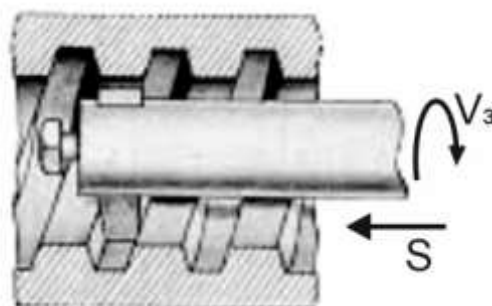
Схема обробки внутрішньої прямокутної гвинтової поверхні різцями.
